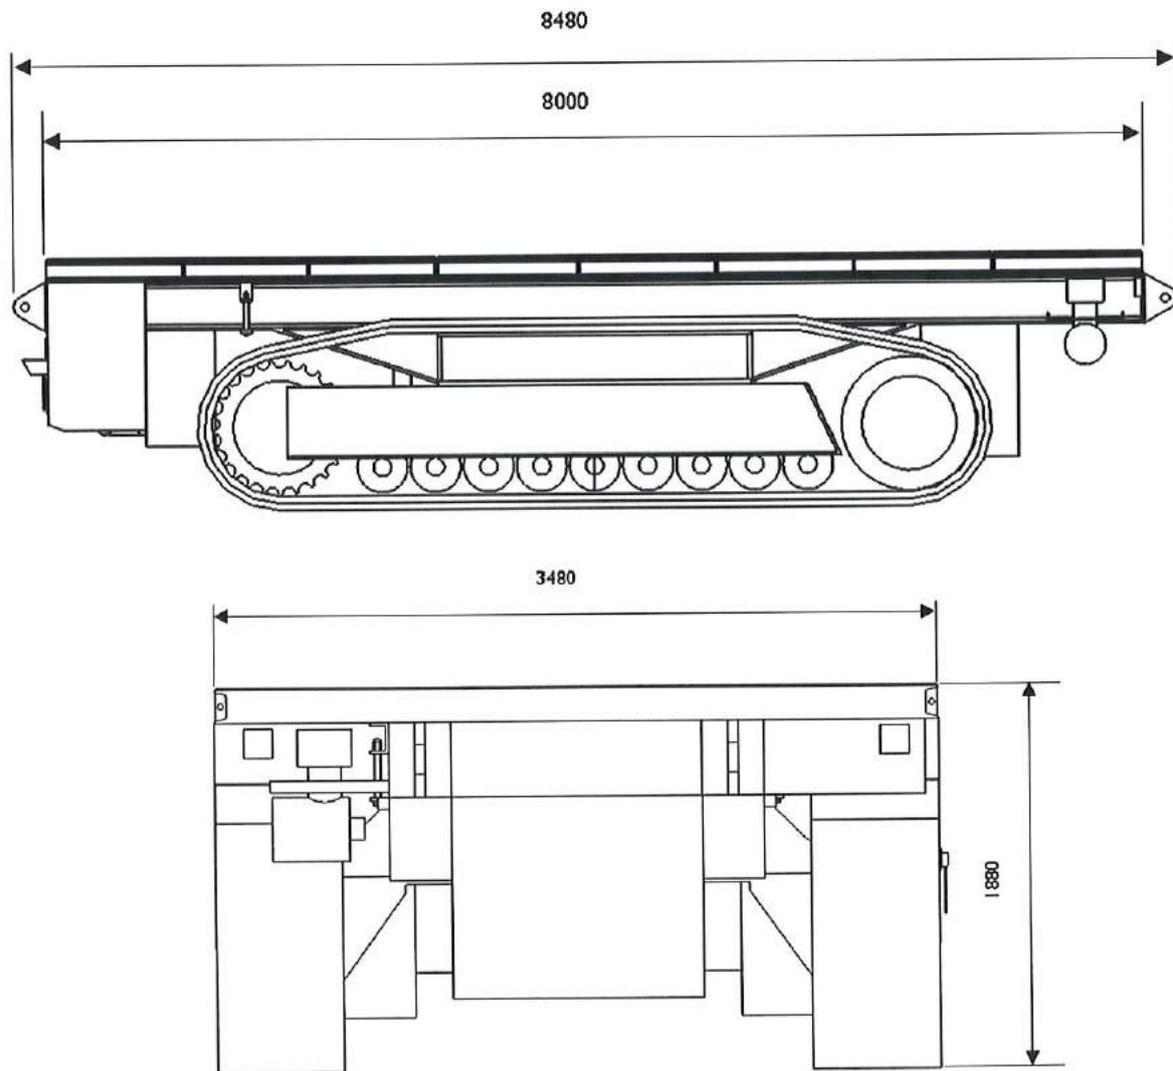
Aplicaciones en vigas de grandes dimensione
